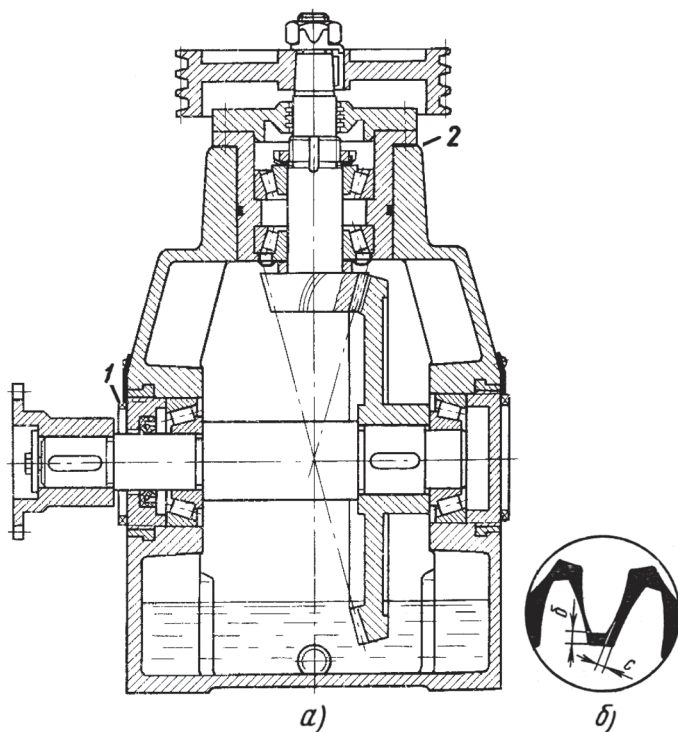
Регулировка зазоров в зацеплении конических колес:
